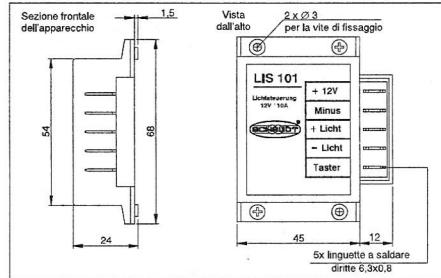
Disegno quattro del dimmer LIS 101 (dimensioni in mm)
